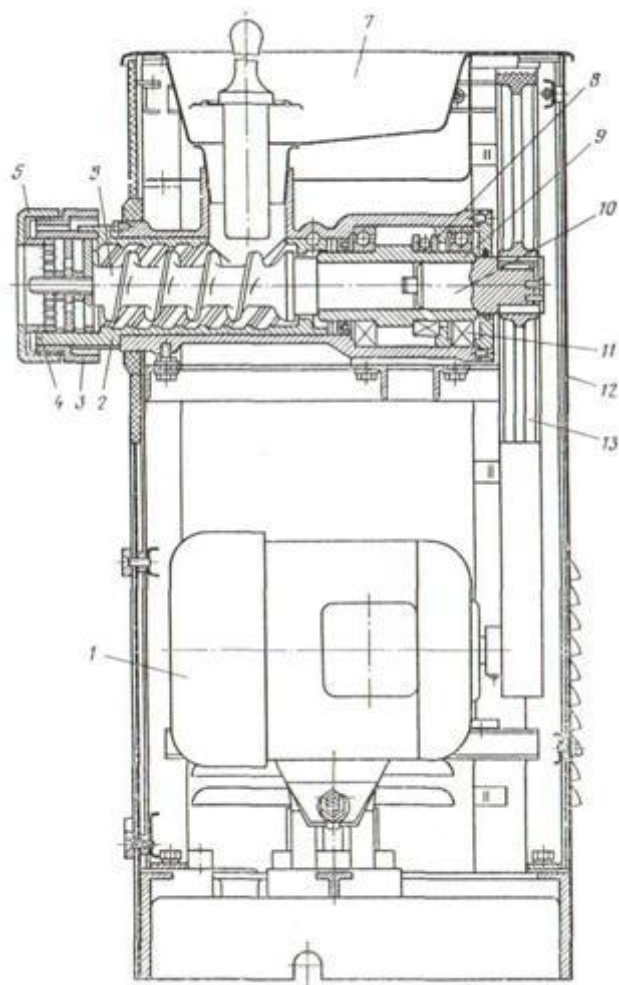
Вовчок МИМ-105М: 1 – електродвигун; 2 - робоча камера; 3 – нерухома гайка; 4 – упорне кільце; 5 – притискна гайка; 6 – шнек; 7 – бункер; 8 – упорний шарикопідшипник; 9 – втулка; 10 – вал; 11 - радіальний шарикопідшипник; 12 – корпус; 13 – клинопасова передача.
